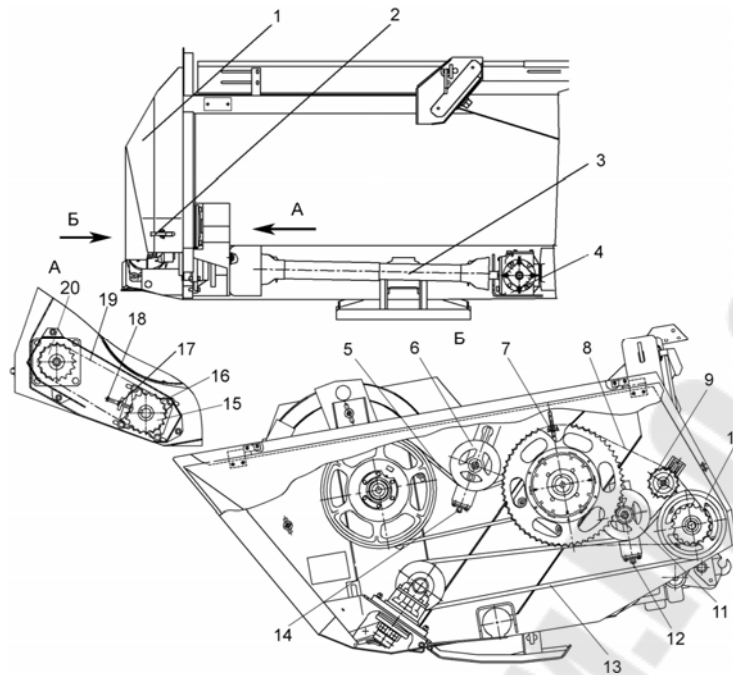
Приводы жатки: 1 – ограждение; 2 – защелка; 3 – вал карданный; 4 – редуктор; 5 – передача привода мотвила клиноременная; 6, 9, 11 – устройства натяжные; 7, 17 – гайки; 8 – передача привода шнека цепная; 10 – контрпривод; 12, 14, 18 – болты регулировочные; 13 – передача привода режущего аппарата ремная; 15 – звездочка ведущая; 16 – опора; 19 – передача цепная; 20 – звездочка ведомая
